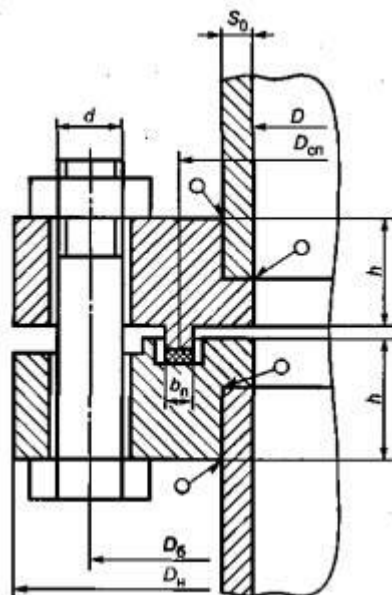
Фланец корпуса и крышки аппарата
